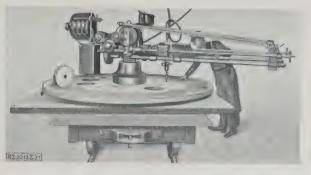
Halbselbsttätige Leuchtgasflammen-Schneidmaschine zum Zuschneiden von Blechplatten.
